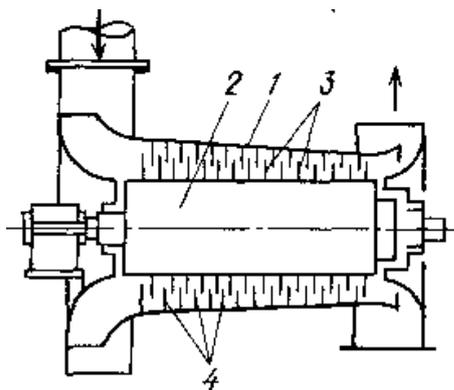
Осевой компрессор: 1 – корпус (статор); 2 – ротор с лопатками; 3, 4 – неподвижные лопатки статора
